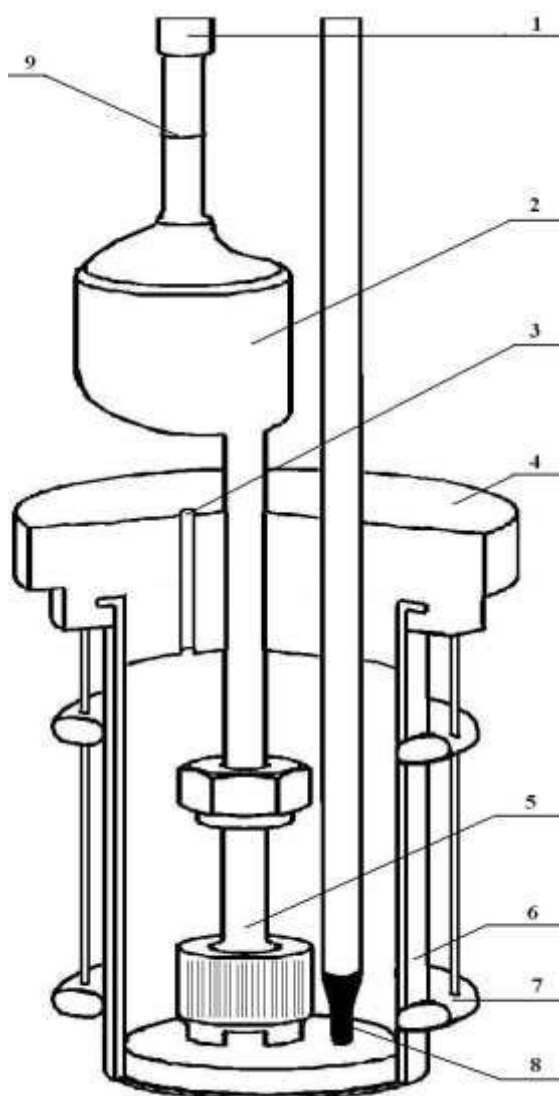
Внешний вид и схема сборки фильтрующего элемента
